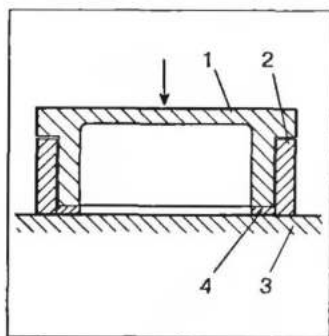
Притирка торцев поршневого кольца на плите: 1 — прижим; 2 — обойма; 3 — плита; 4 — кольцо
